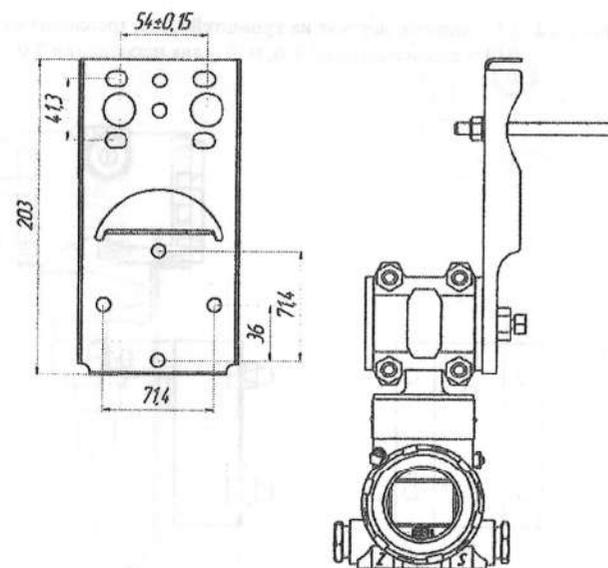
Плоский кронштейн для крепления на трубе (B06), габаритные и присоединительные размеры
